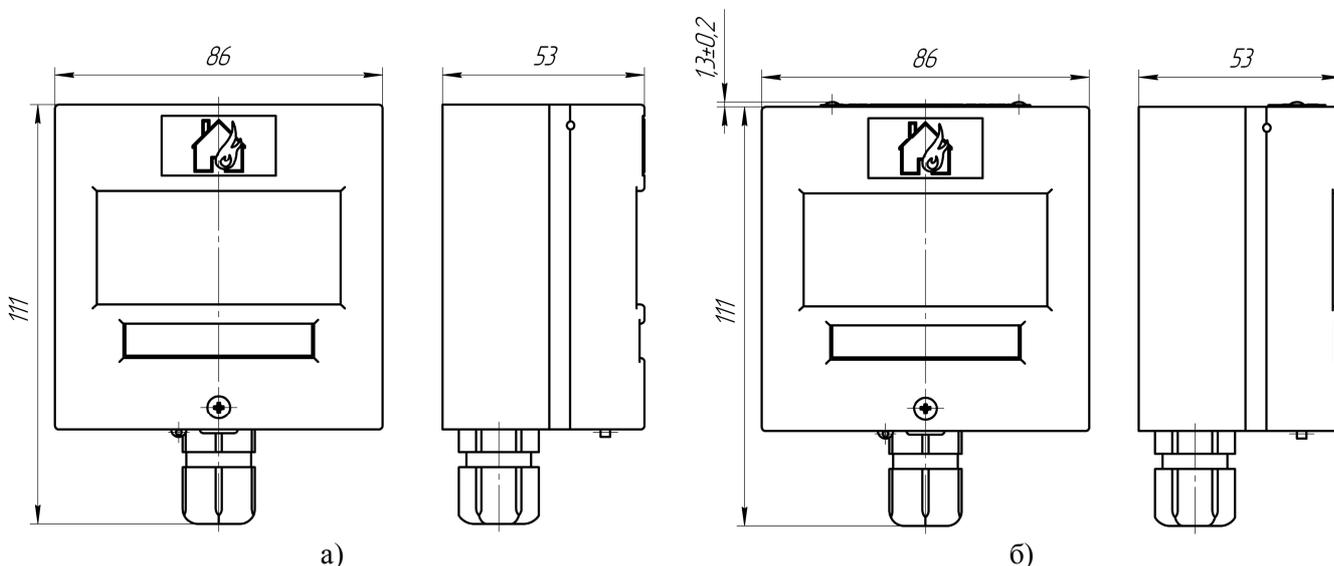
Внешний вид и габаритные размеры извещателей ИПРА-01 (а) и ИПРА-01В (б), размеры в мм
